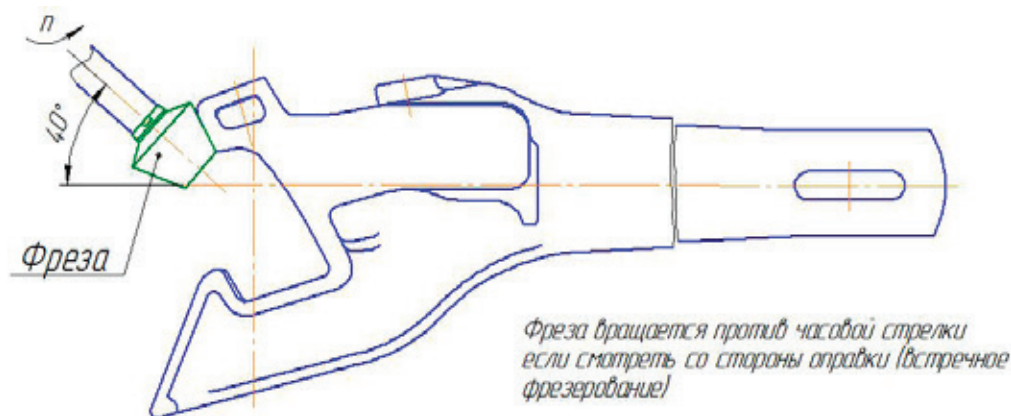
Схема фрезерования ударной поверхности малого зуба
